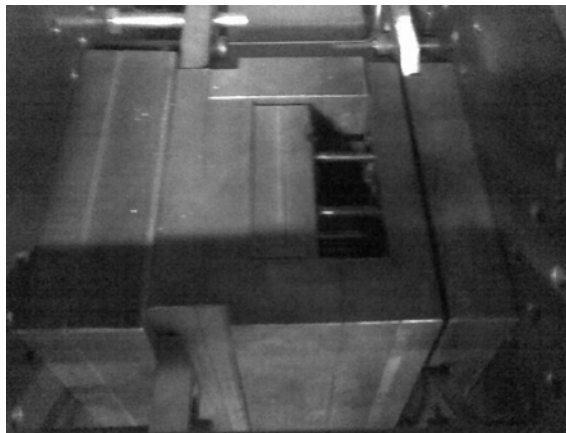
Placas portamoldes vistas desde arriba, montadas en la máquina
